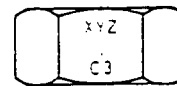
Beispiele für die Kennzeichnung von Schrauben
